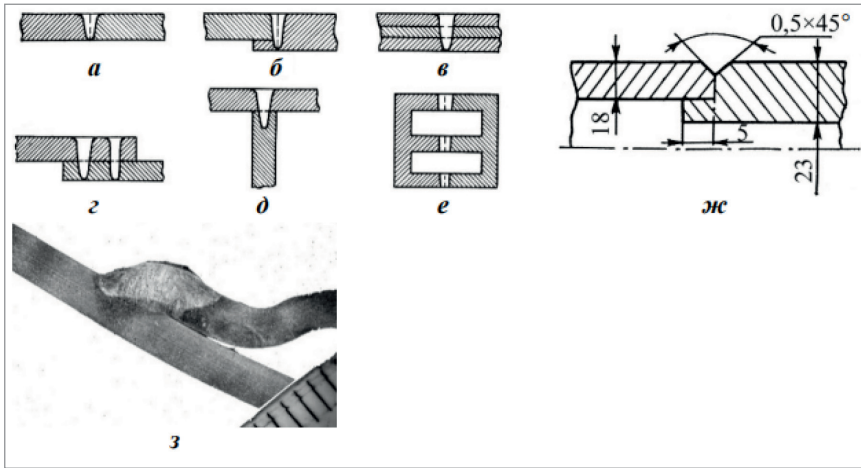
Деякі типи з'єднань при ЕПЗ: а, б – стикові; в, г – з прорізними швами; д – таврове з прорізним швом; е – однопрохідне зварювання трьох стиків; ж – стикове з'єднання деталей циліндричної форми; з – з'єднання деталей жарової труби<sup>15</sup>
